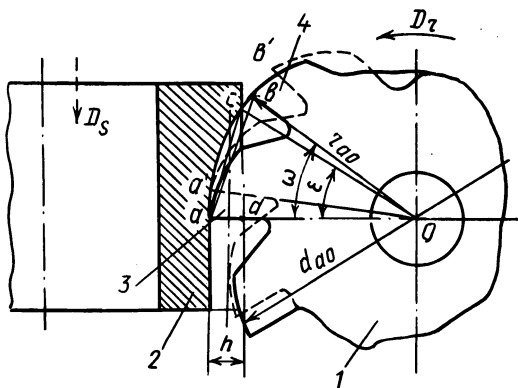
Схема реализации способа фрезерования зубьев цилиндрических зубчатых колес с импульсным движением подачи:
